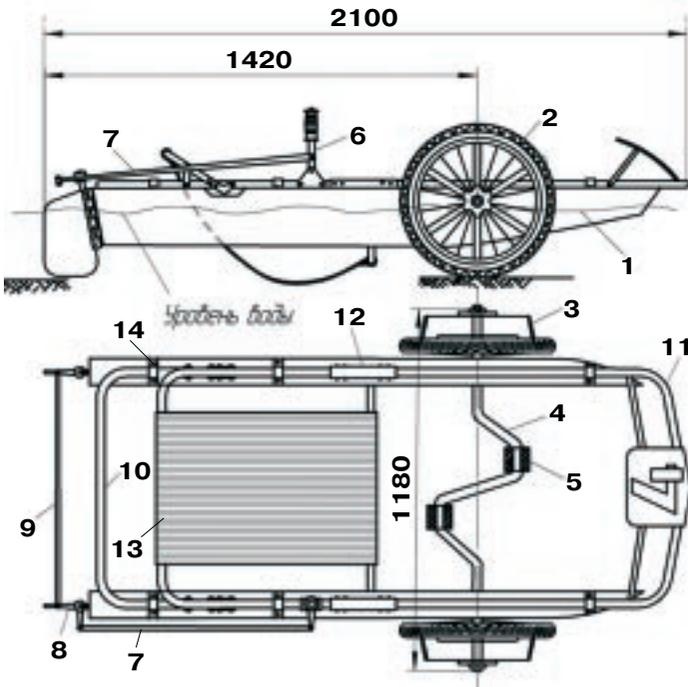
Основные размеры и конструкция: 1 — поплавок; 2 — колесо; 3 — гребные лопасти; 4 — коленвал; 5 — педаль; 6 — рычаг управления; 7 — рулевая тяга; 8 — поворотный кронштейн; 9 — тяга рулевой трапеции; 10 — кормовая половина рамы; 11 — носовая половина рамы; 12 — соединительная трубка; 13 — сиденье; 14 — пластина.
